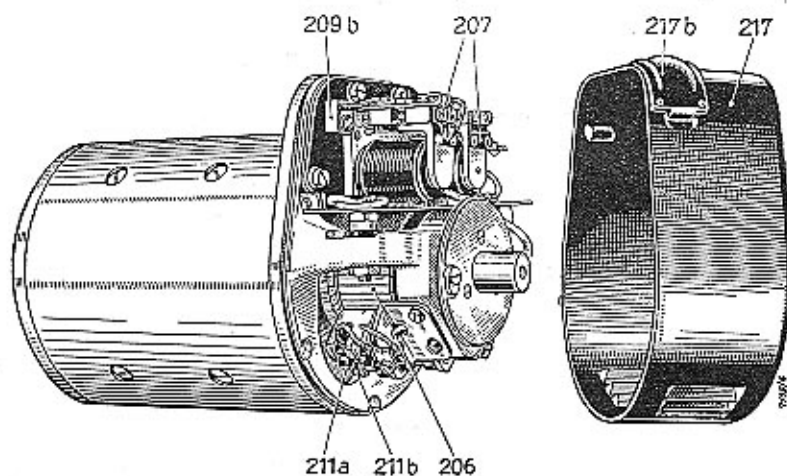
Lichtmaschine mit eingebautem Regler-Schalter
